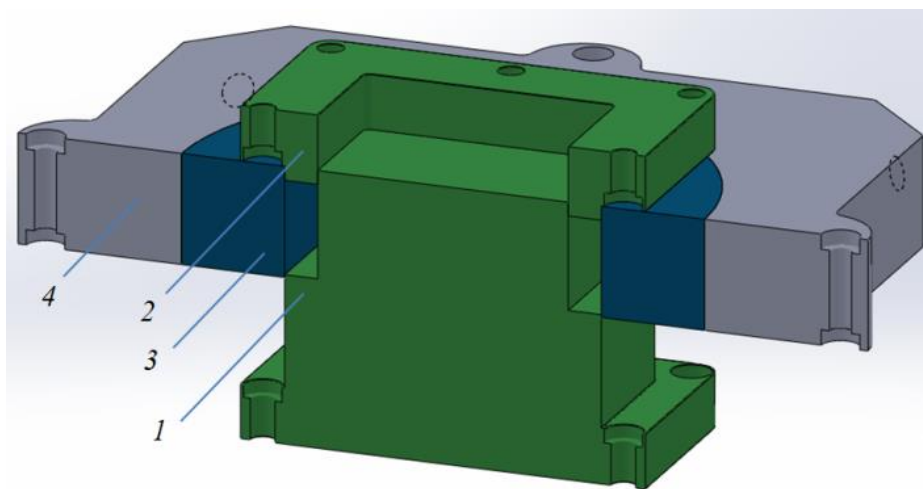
Внешний вид (в разрезе) пресс-формы, реализующей представленный эскизный проект
